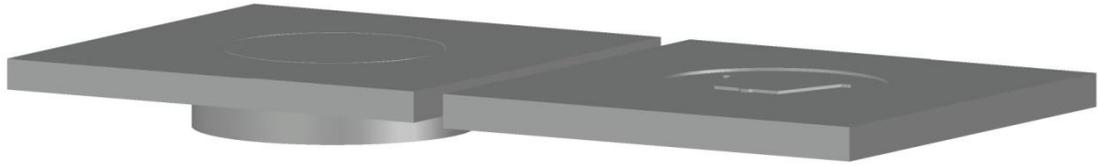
Molde para la pieza 1.1 tapa grande. Detalle inferior.
